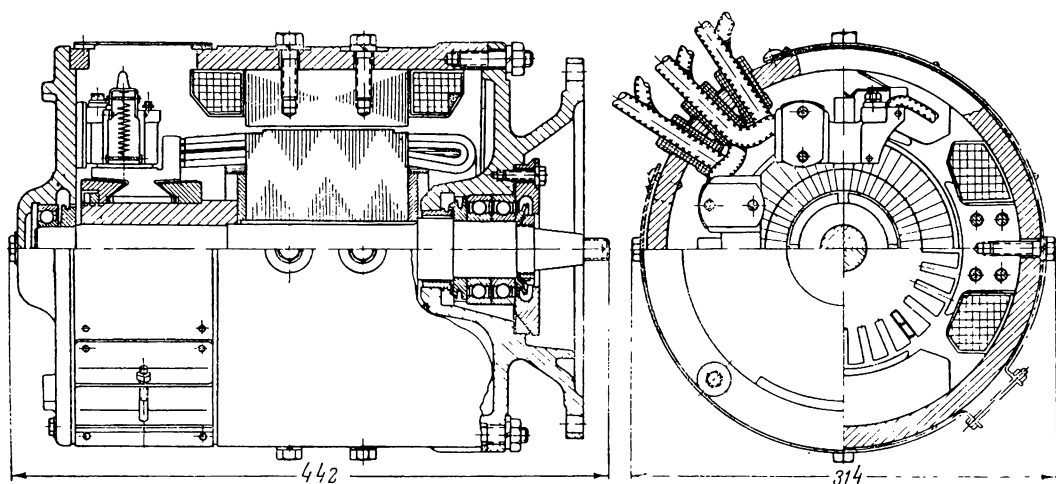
Двигатель типа ДК-255 с независимой подвеской.
